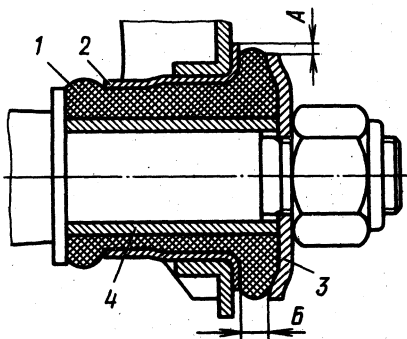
Проверка состояния резино-металлического шарнира рычага передней подвески автомобиля «Жигули»:
